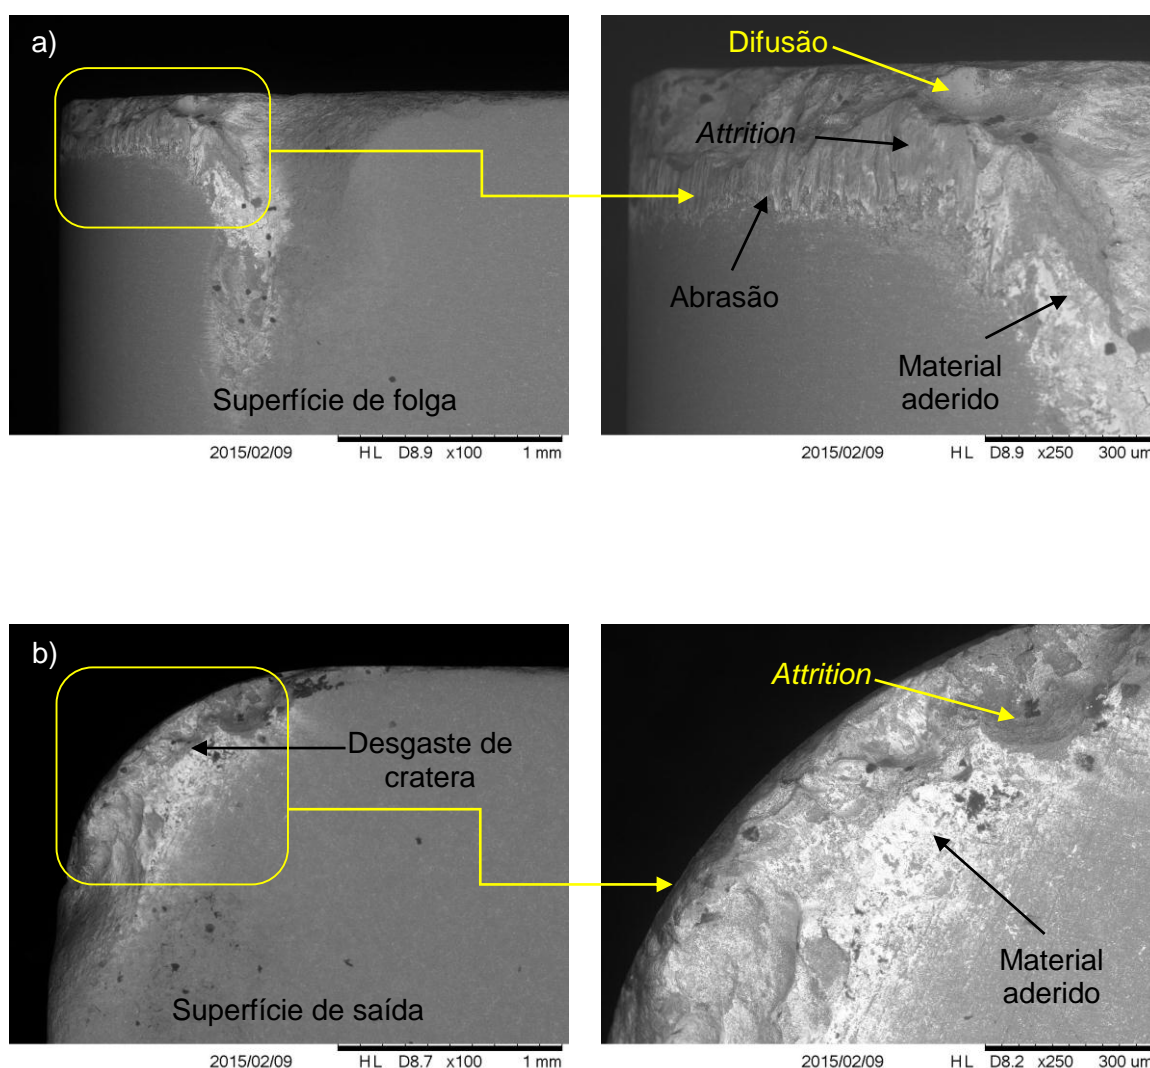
Fotografias obtidas através do MEV das ferramentas *whisker* após a usinagem do Inconel 718 a seco. (a) superfície de folga e (b) superfície de saída
